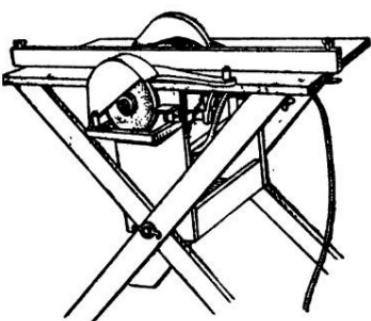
Переносный комбинированный станок — дисковая пила-точило.
